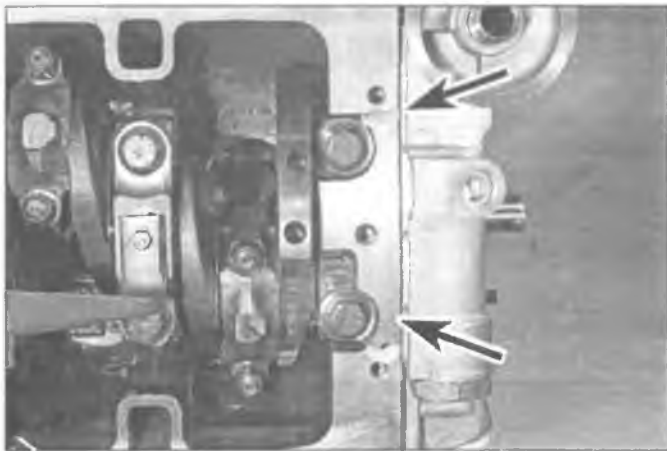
Нанесите валик герметика на стыки между крышкой переднего коренного подшипника и блоком цилиндров (отмечены стрелками), причем обязательно заполните герметиком канавки в крышке.
